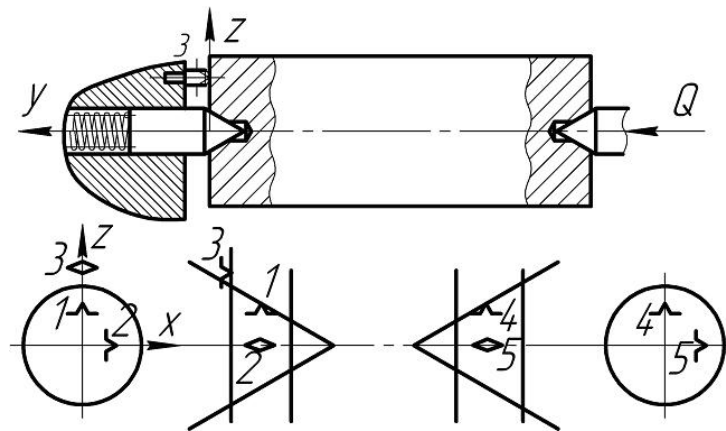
Встановлення деталі на плаваючий центр
